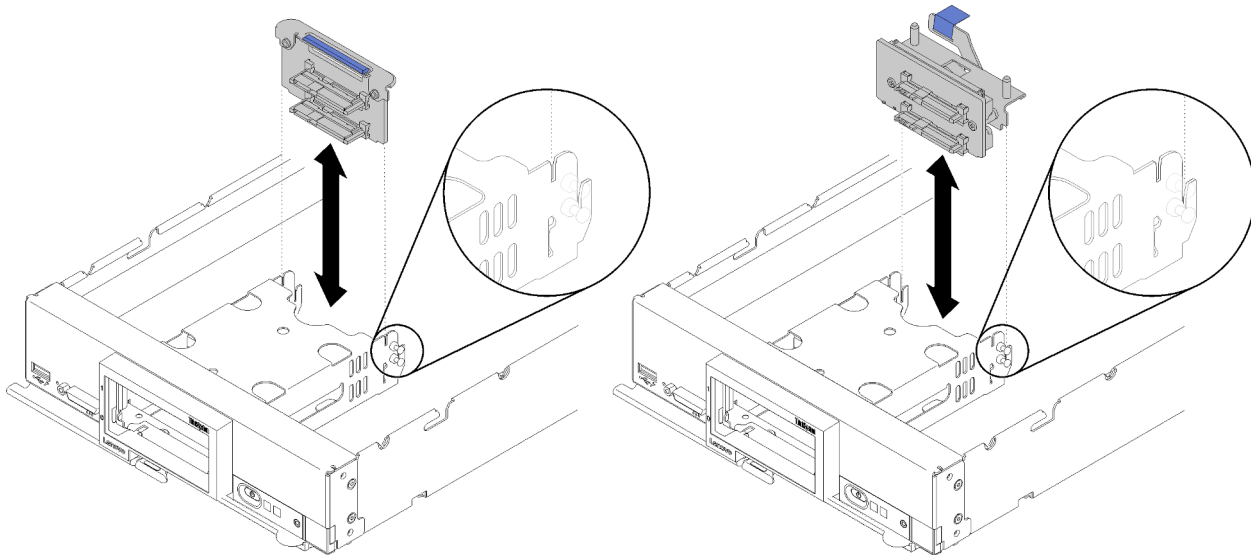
Installation d'un fond de panier d'unité 2,5 pouces
